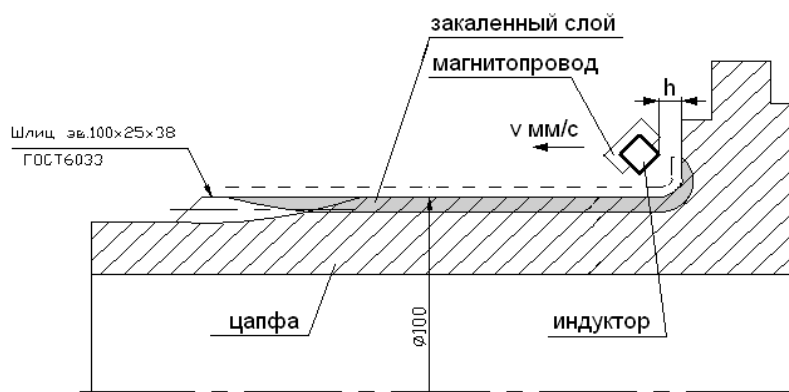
Схема закалки наружной цилиндрической поверхности с выходом на галтель непрерывно-последовательным способом при движении индуктора относительно детали
